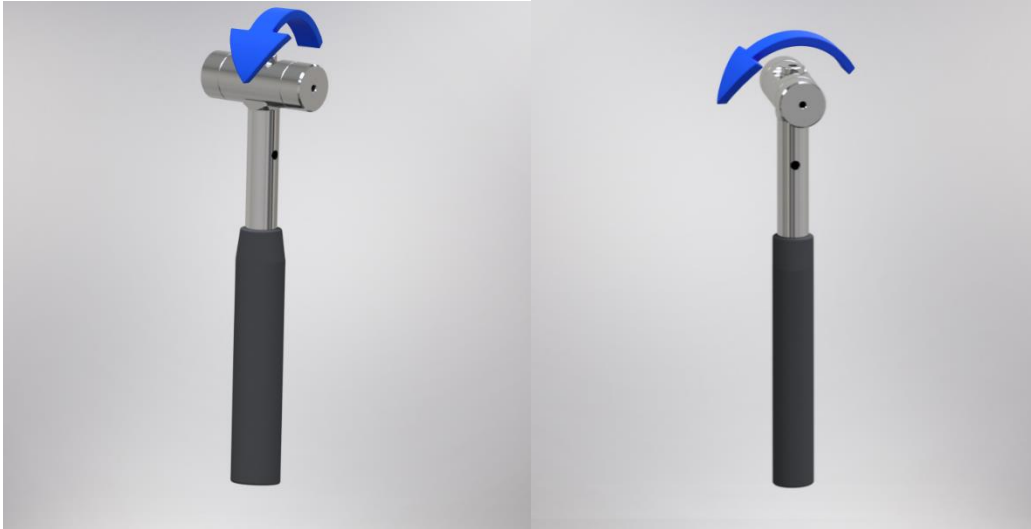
Diferentes planos de vibración, plano en T y plano de cabeceo.
